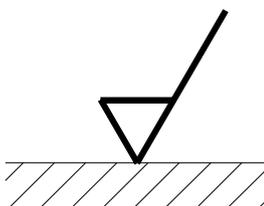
símbolo de estado de superfície que exige retirada de material.
